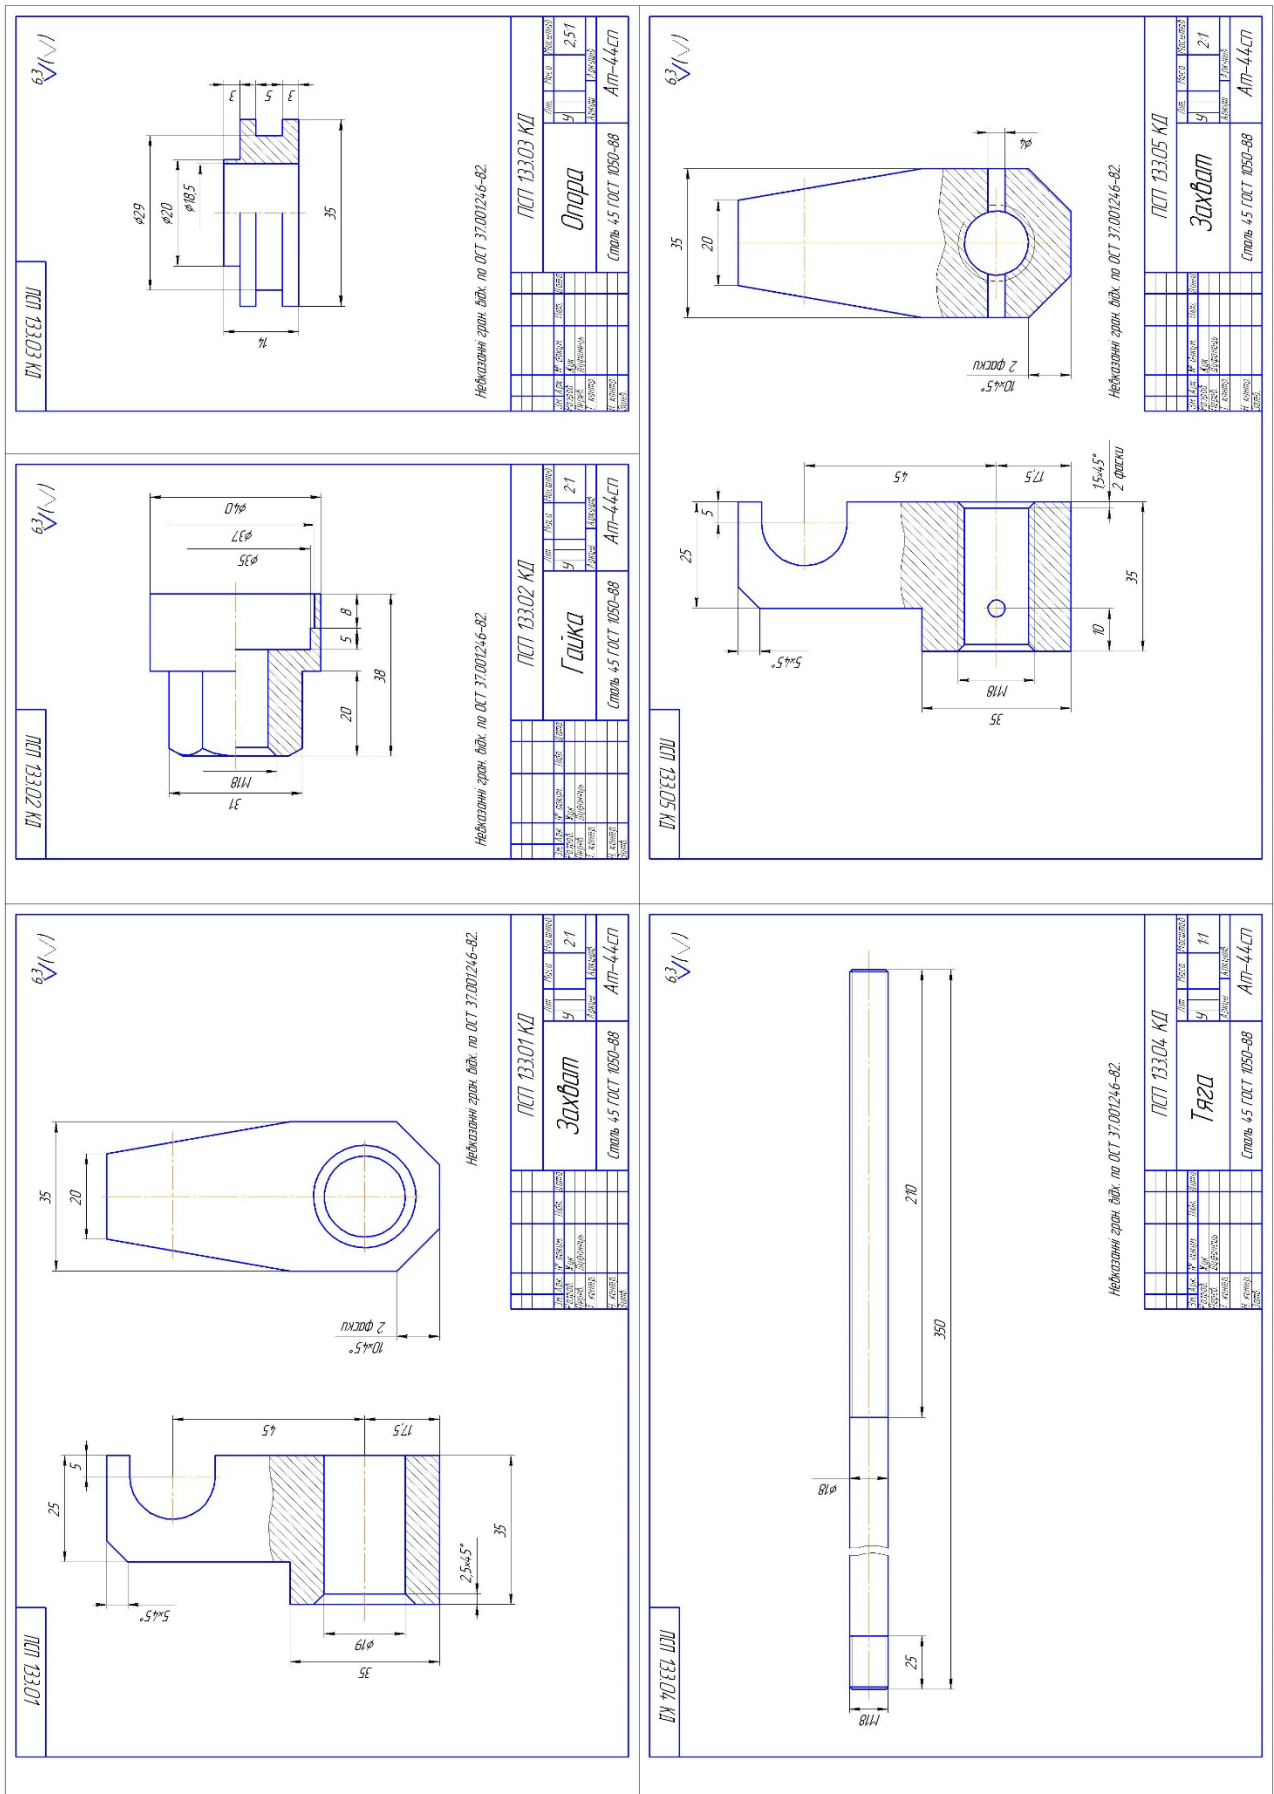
Пристрій для стяжки пружини підвіски автомобіля деталювання.
